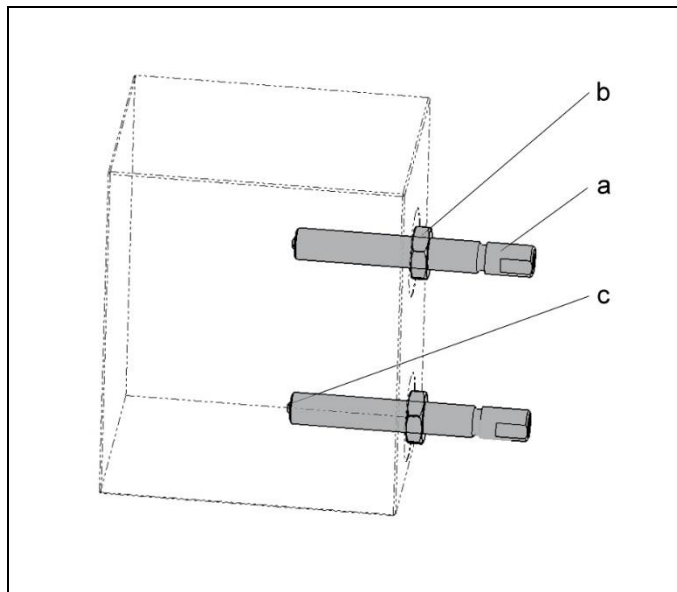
Componentes (principio de montaje en una brida de sujeción)
